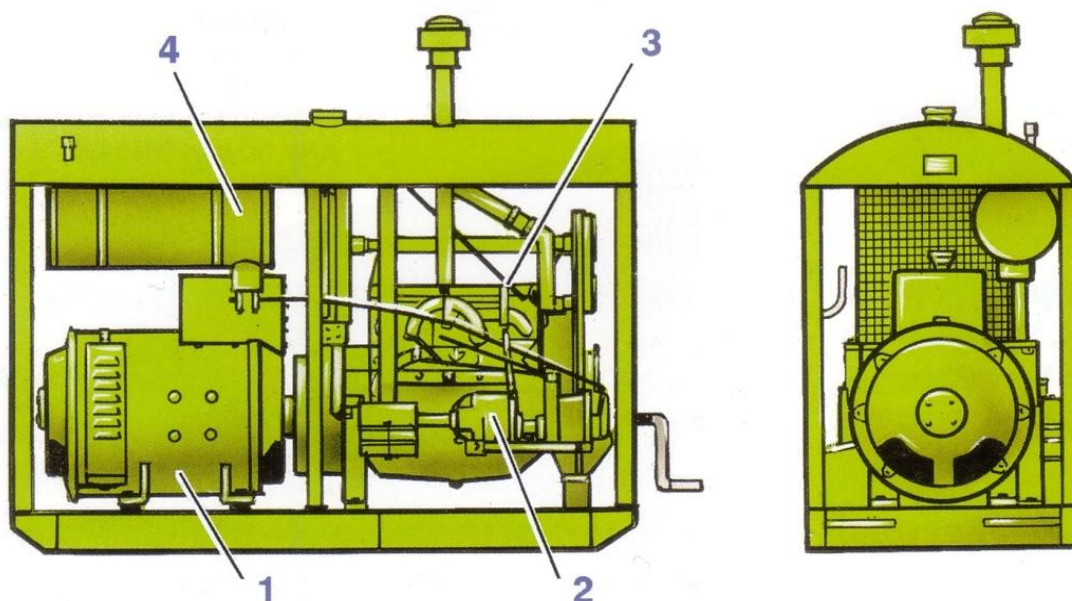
Внешний вид сварочного агрегата: 1 – генератор; 2 – двигатель; 3 – регулятор скорости вращения; 4 – бак с горючим
